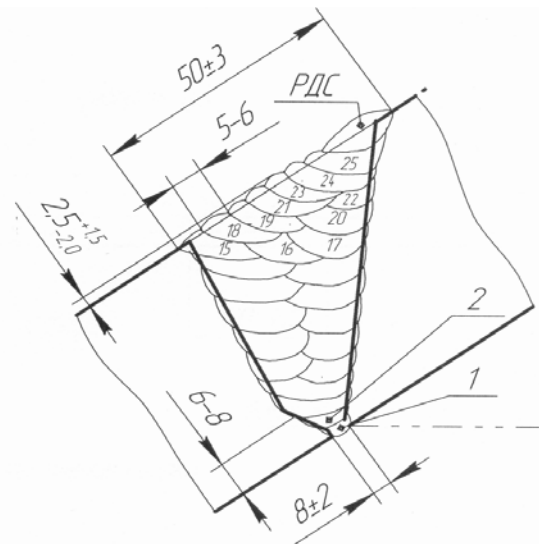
Сварное соединение стали 10ХСНД толщиной 50 мм. Автоматическая сварка проволокой Св-10НМА под флюсом АН-47
